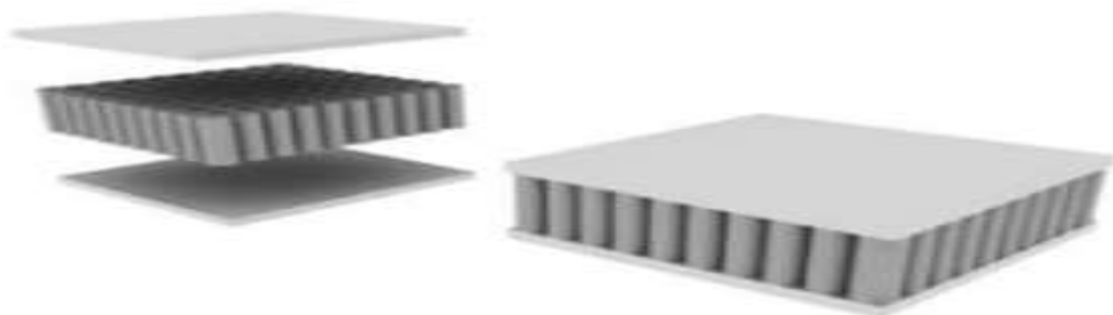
Estructura de un material compuesto con refuerzo tipo sándwich. [8]
